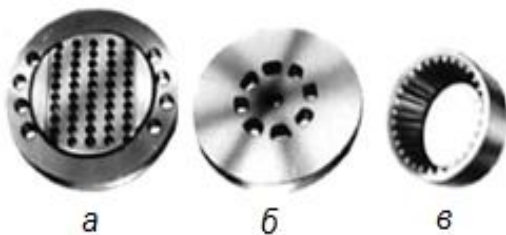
Зразки виробів: а – сідло клапана компресора; б – магнітопровід ротора; в – муфта внутрішнього зчеплення
